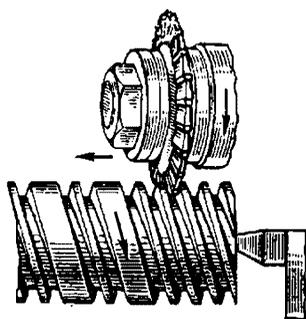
Фрезерование резьбы дисковой фрезой
